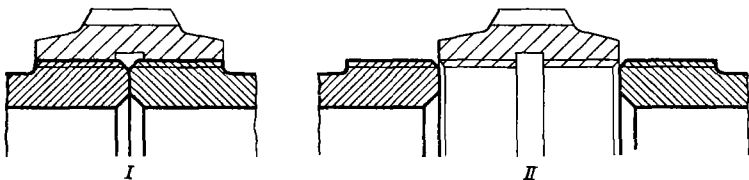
Затяжка внасадной детали на валу гайкой с резьбой противоположного направления:
